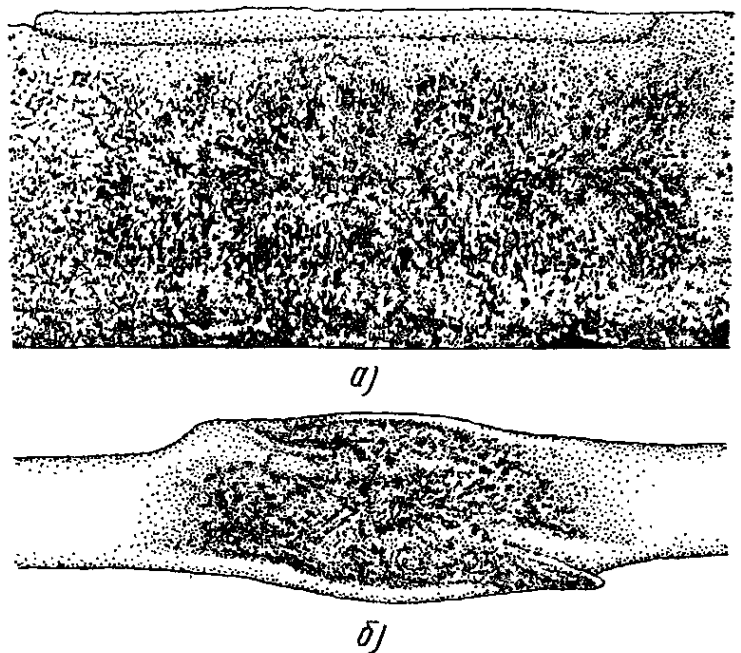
Макроструктура после сварки с накладками (*а*) и с раздавливанием кромок (*б*)
